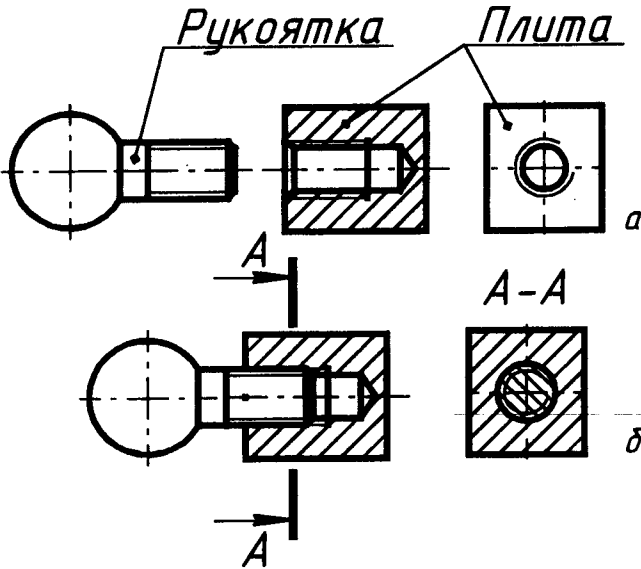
Пример резьбового соединения: а) изображение соединяемых деталей; б) резьбовое соединение
